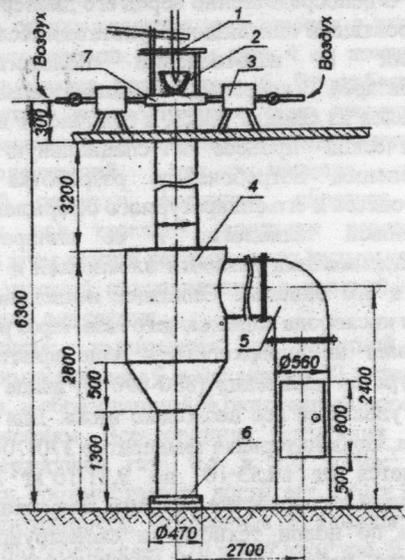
Принципиальная схема установки для получения свинцового порошка: 1-игольчатый клапан; 2-тигель; 3-нагреватели воздуха; 4-распылительная камера; 5-вытяжная вентиляция; 6-узел выгрузки порошкового материала; 7-форсуночный узел.
